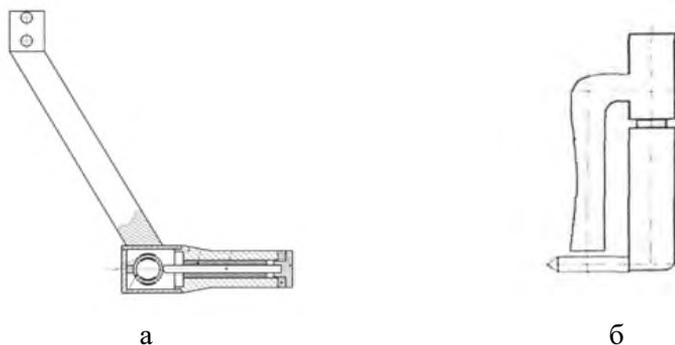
Непрерывные твердомеры: твердомер С. В. Машкова (а); твердомер Р. Р. Шакирова(б)
